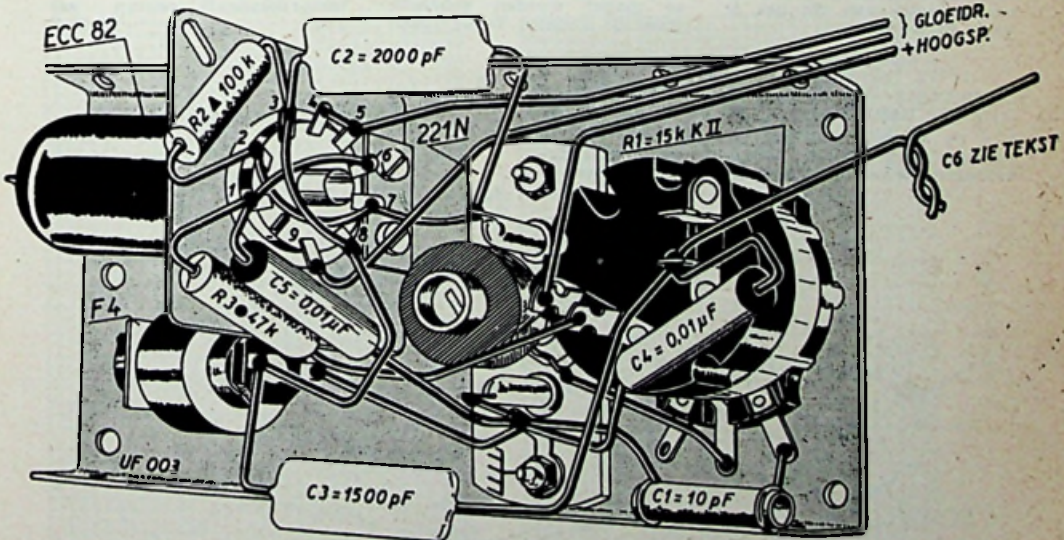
HET MONTAGEPLAN VAN DE UN-41
